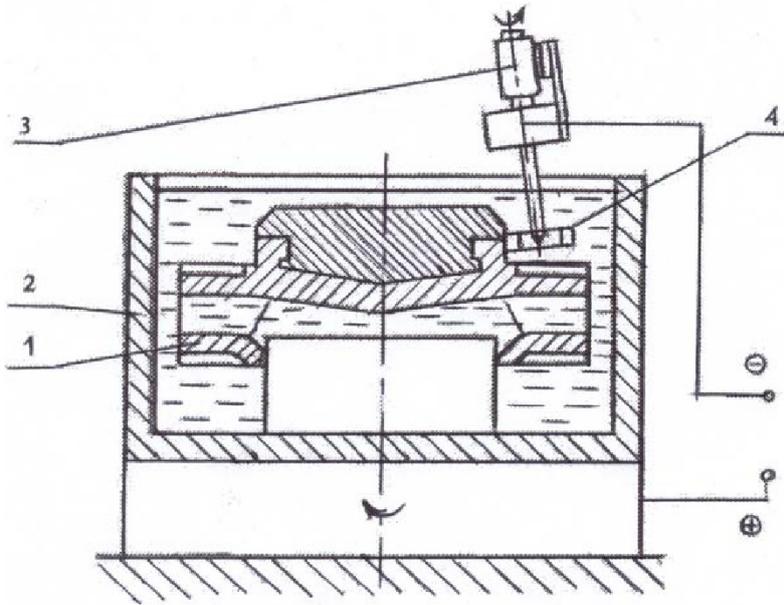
Схема электроконтактной черновой обработки рабочих колес на станке мод. МЭ303Ф1 по а.с.228813: 1- заготовка, 2- ванна с технической водой, 3- шпиндель станка, 4- электрод-инструмент
